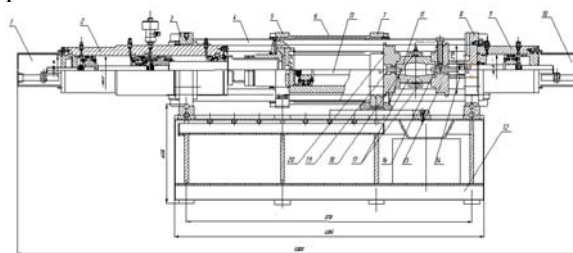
Конструкция прессы: 1 – датчик перемещения штока мультипликатора; 2 – гидроцилиндр силового замыкания; 3, 8 – плиты опорные; 4 – колонна; 5, 7 – плиты подвижного блока; 6 – гильза-стяжка; 9 – гидроцилиндр прессования; 10 – датчик перемещения штока; 11 – башмак опорный; 12 – станина; 13 – гидроцилиндр встроенный; 14 – втулка опорная; 15 – основание неподвижное; 16 – чаша заливочная; 17 – матрица разъемная; 18 – кольцо с выходом к вакуумному насосу; 19 – плунжер прессующий; 20 – основание подвижное
